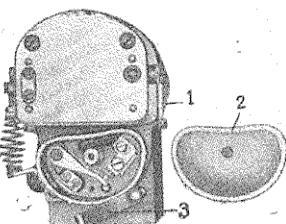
Dynamo Bosch, couvercle du rupleur enlevé.
